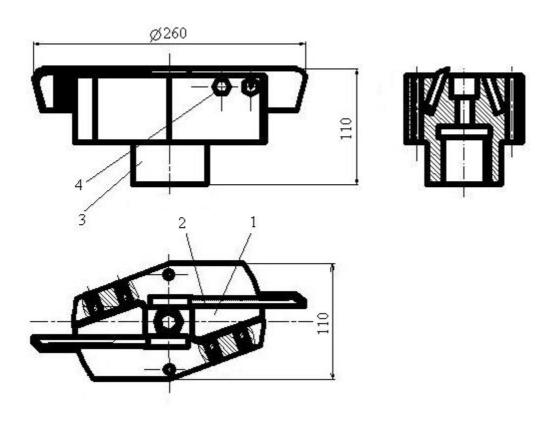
Фреза: 1 – клин; 2 – нож; 3 – корпус фрезы; 4 – винты
